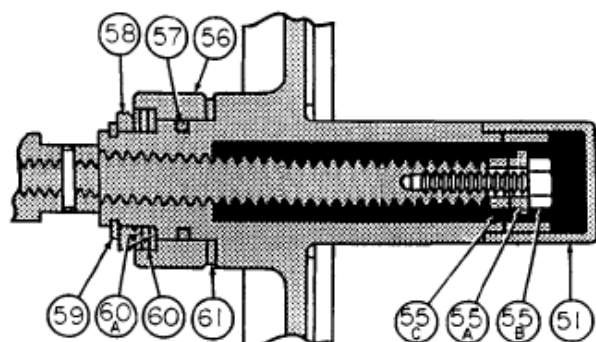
Деталировочный чертеж маховика. Приводы размера В и С
